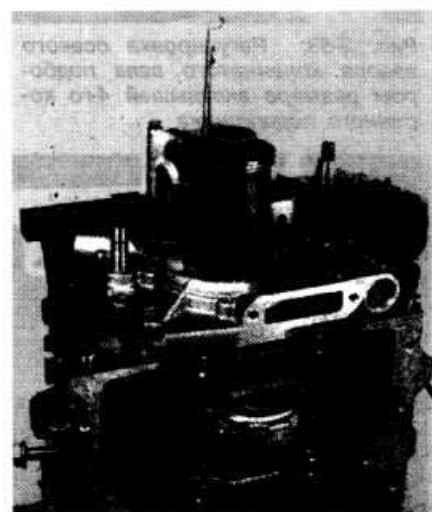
Центрирование масляного насоса относительно коленчатого вала с помощью приспособлений BMW 11.4.201 и 11.4.202/203
